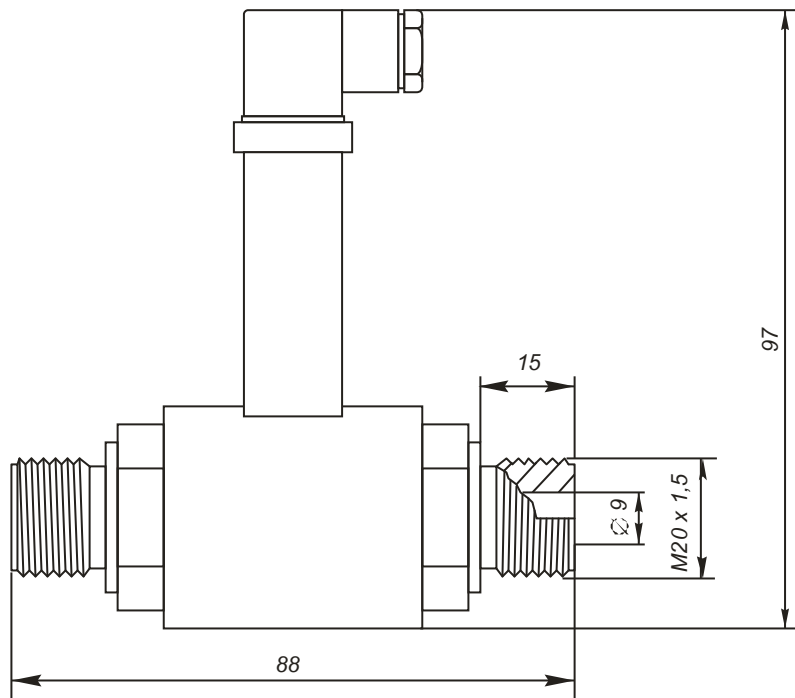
Монтажный чертеж малогабаритного датчика разности давлений КОРУНД-ДД-Н
